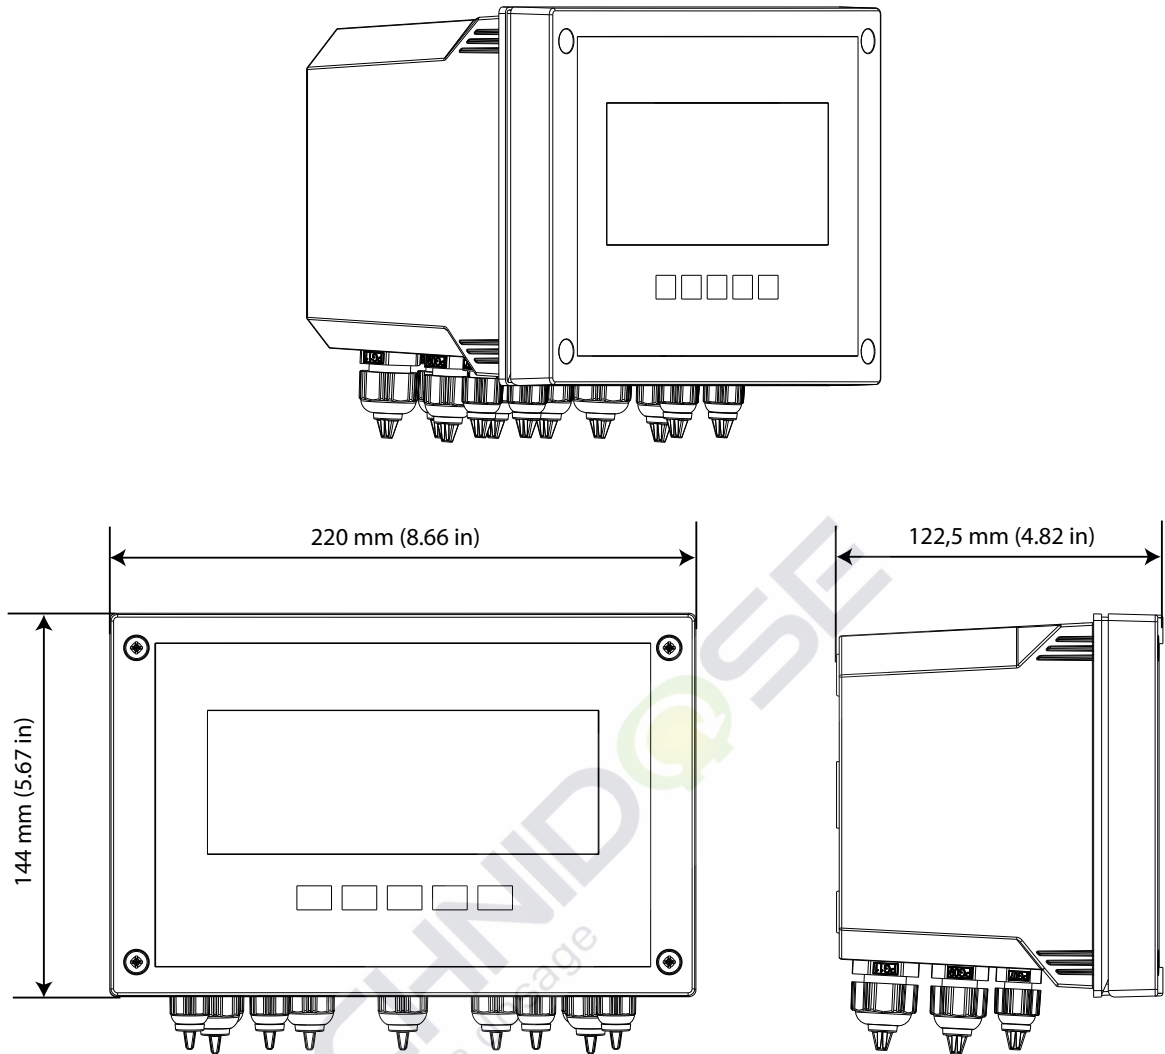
Dimensions et encombrement du dispositif à montage mural
